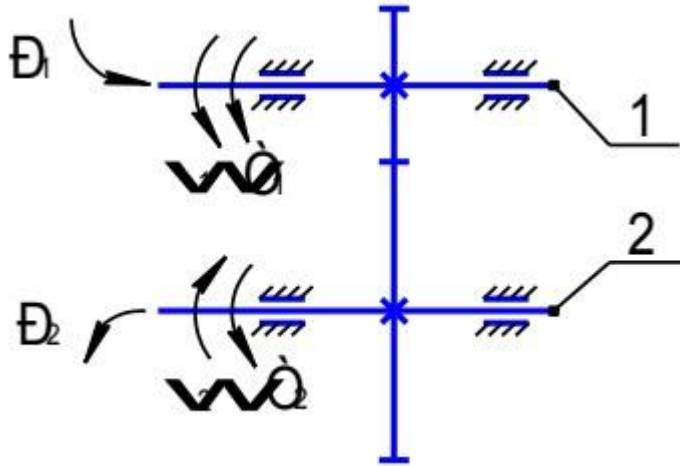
Схема ступеня механічної знижувальної передачі обертового руху
